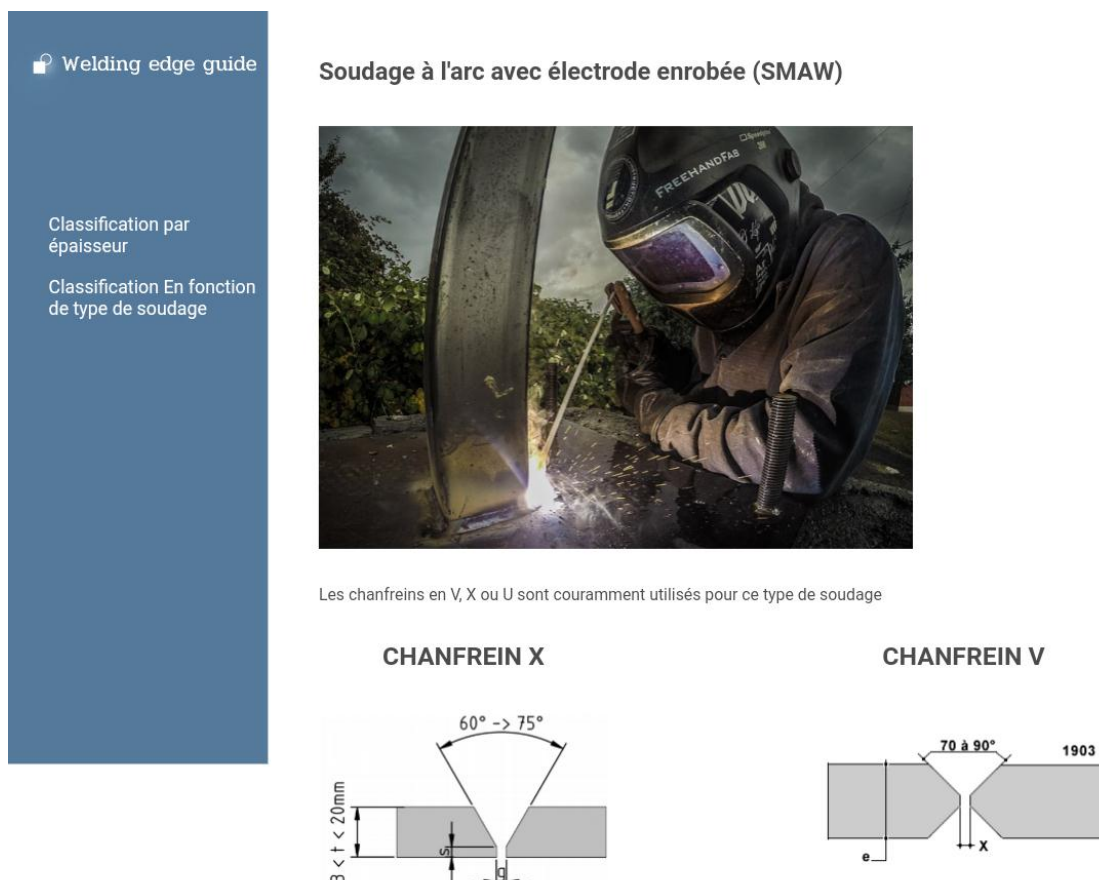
Classification par type de soudage (Soudage à l'arc)
